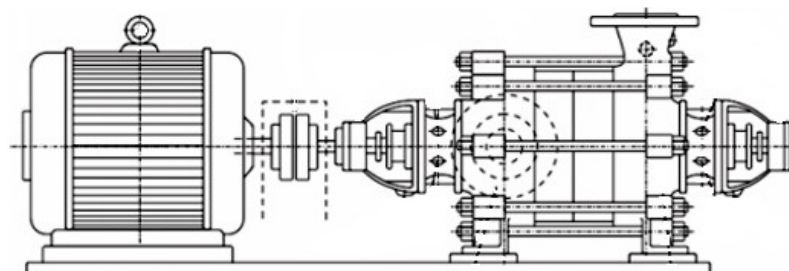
Conjunto motor elétrico e bomba centrífuga
